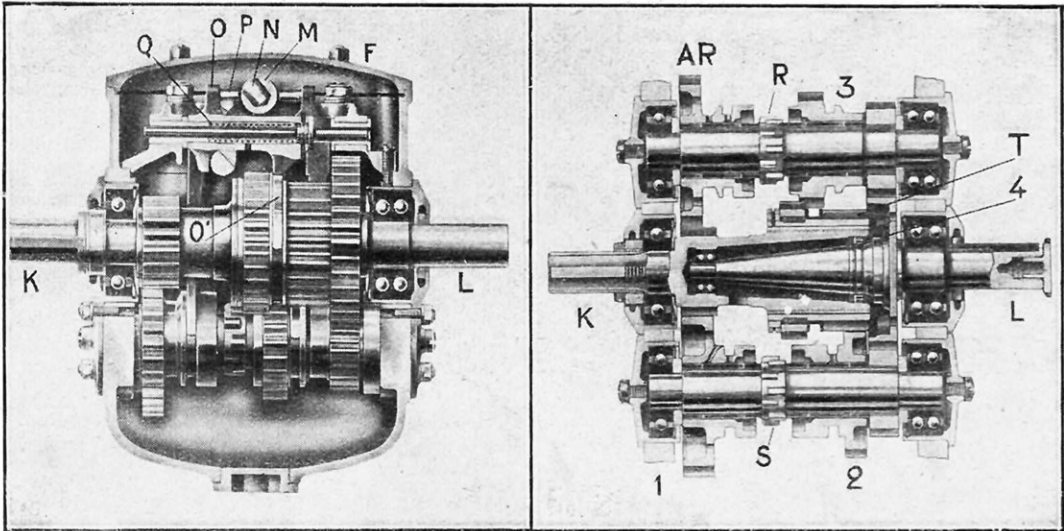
DISPOSITION GÉNÉRALE DES ENGRENAGES ET DES ORGANES DE COMMANDE
